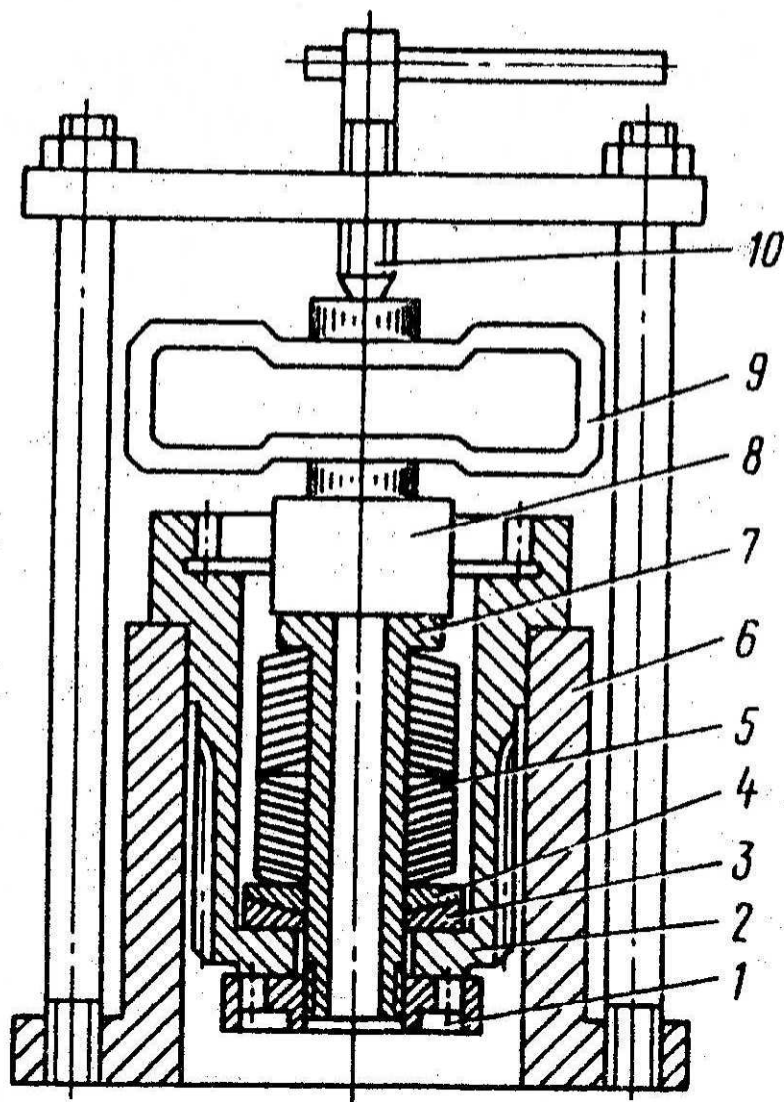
Сборочный узел для предварительного нагружения пакета тарельчатых пружин
